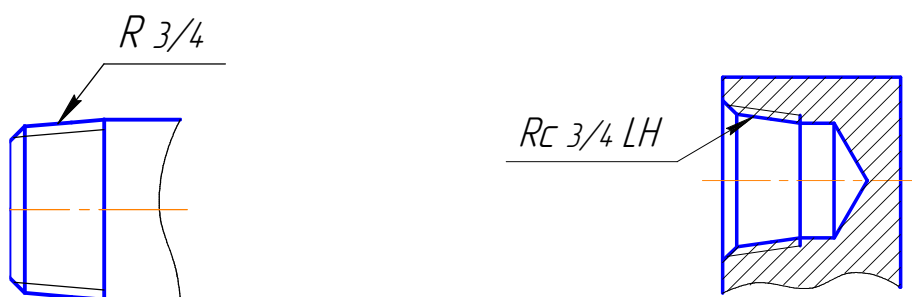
Резьба трубная коническая: а – на стержне; б – в отверстии
